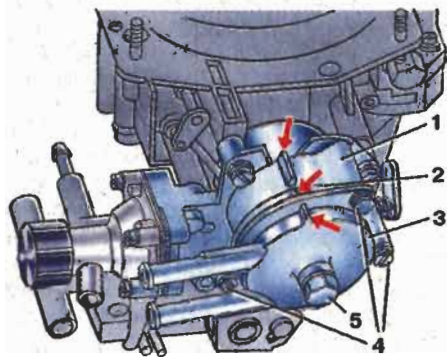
Проверка правильности установки биметаллической пружины полуавтоматического пускового устройства: 1 – корпус пускового устройства; 2 – корпус биметаллической пружины; 3 – корпус жидкостной камеры; 4 – винты крепления корпуса биметаллической пружины; 5 – болт крепления жидкостной камеры
